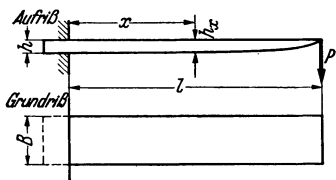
Rechteckfeder. Die Blattstärke verläuft
